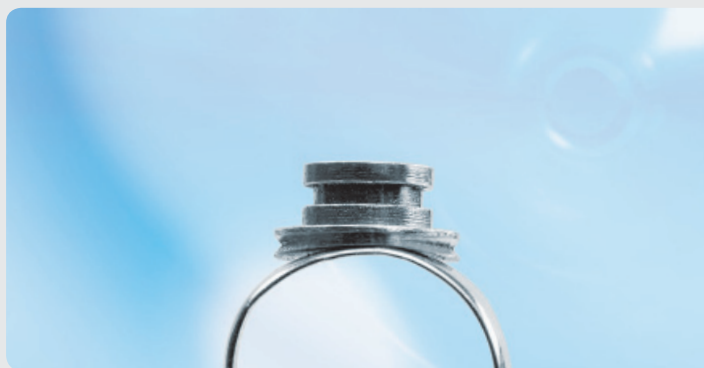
Der Herbst IV Sockel wurde für das Laserschweißen der Form des Prämolaren-Bandes angepasst werden.
